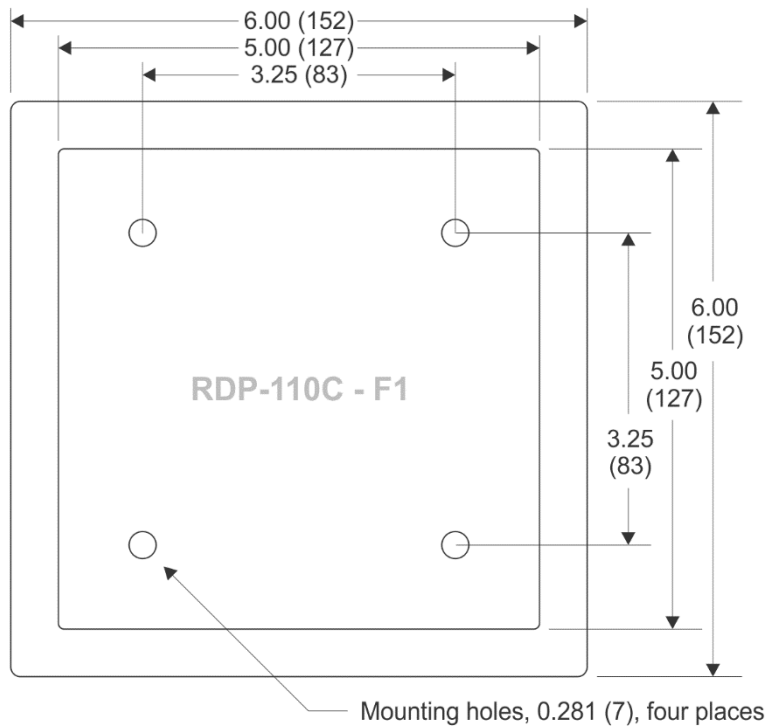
Dimensions de montage, styles arrière, F1 et S1
